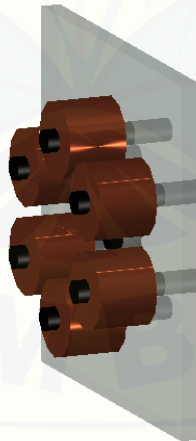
Desain 3 dimensi motor AFPM BLDC rotor ganda
